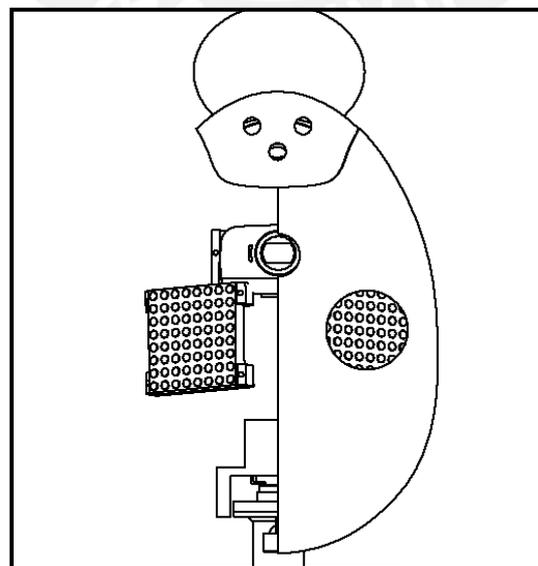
Vista frontal de la cabeza del robot con medio lado expuesto (Fuente: Propia)
